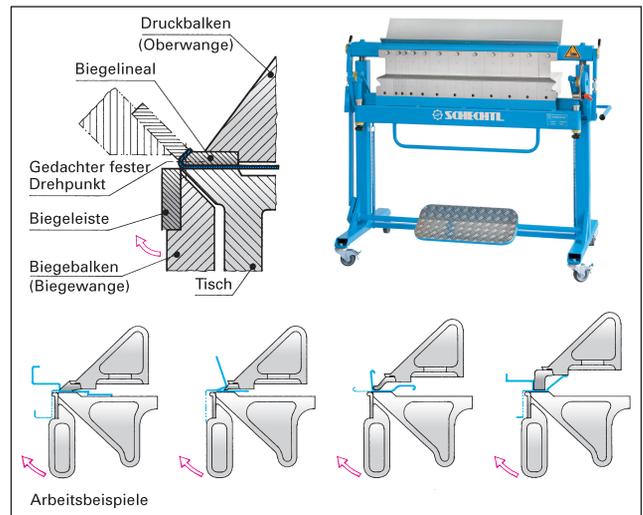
Arbeitsweise einer Schwenkbiegemaschine
